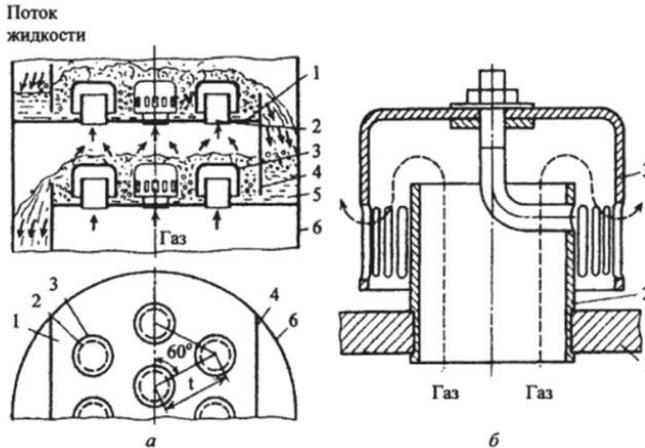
а: Конструкция колпачковой тарелки: 1- тарелка; 2-газовый патрубков; 3- колпачок; 4- сливной патрубок (переливной сегмент); 5-гидрозатвор; 6- корпус колонны.
